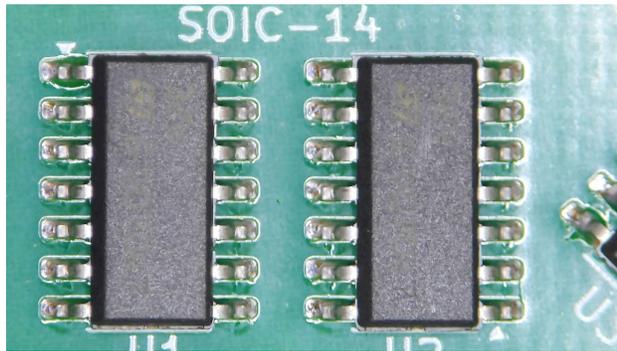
Circuitos integrados con encapsulado SOIC-14 soldados en el cupón.
